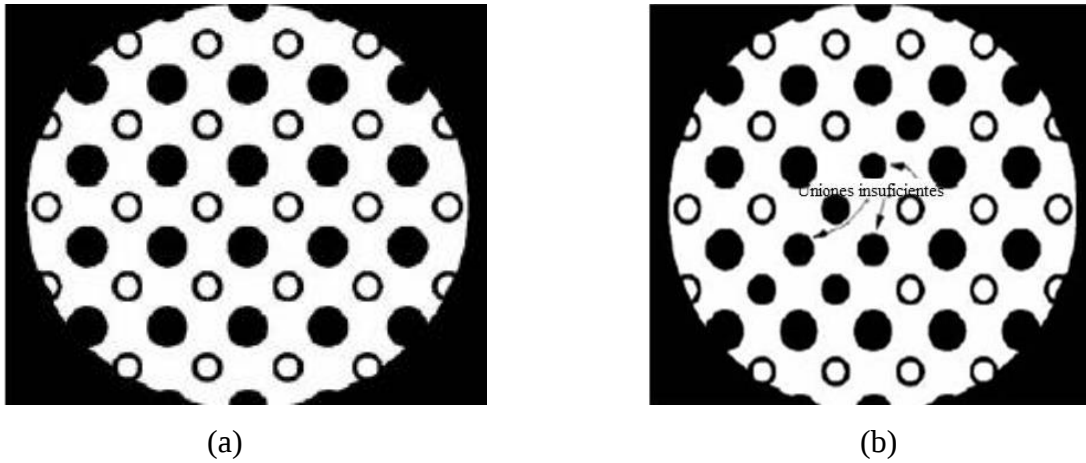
Rayos X de las uniones de soldadura de un BGA,
